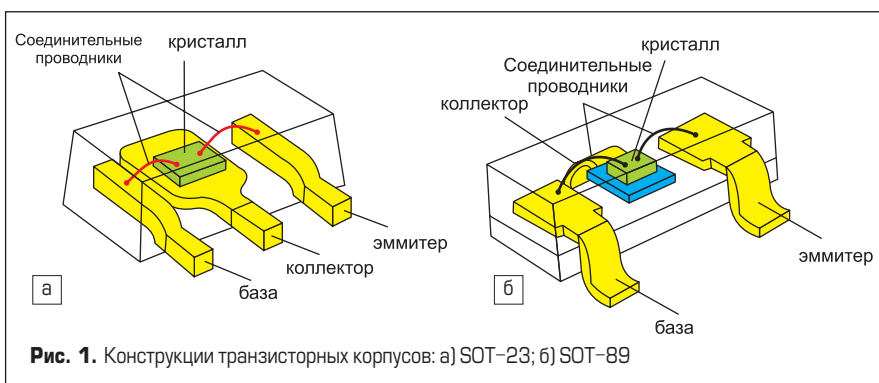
Конструкции транзисторных корпусов: а) SOT-23; б) SOT-89
